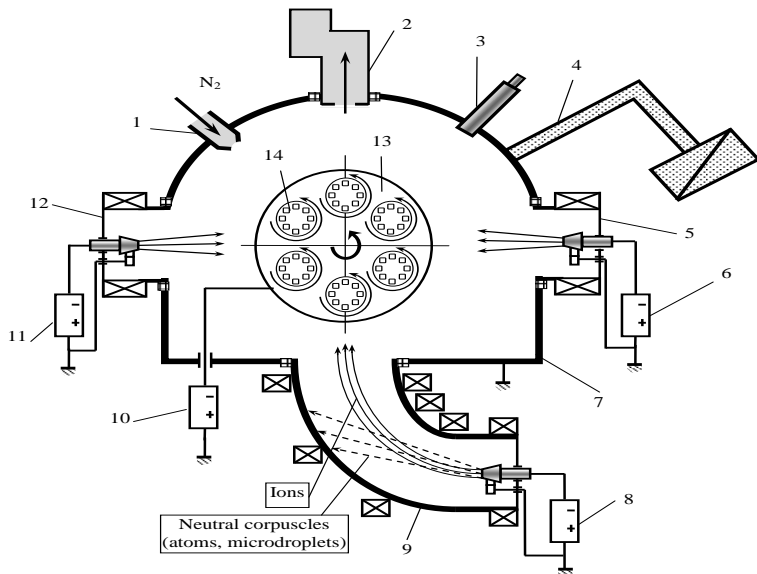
Схема плазменно-дуговой установки ВИТ-2 для нанесения покрытий на режущий инструмент:
